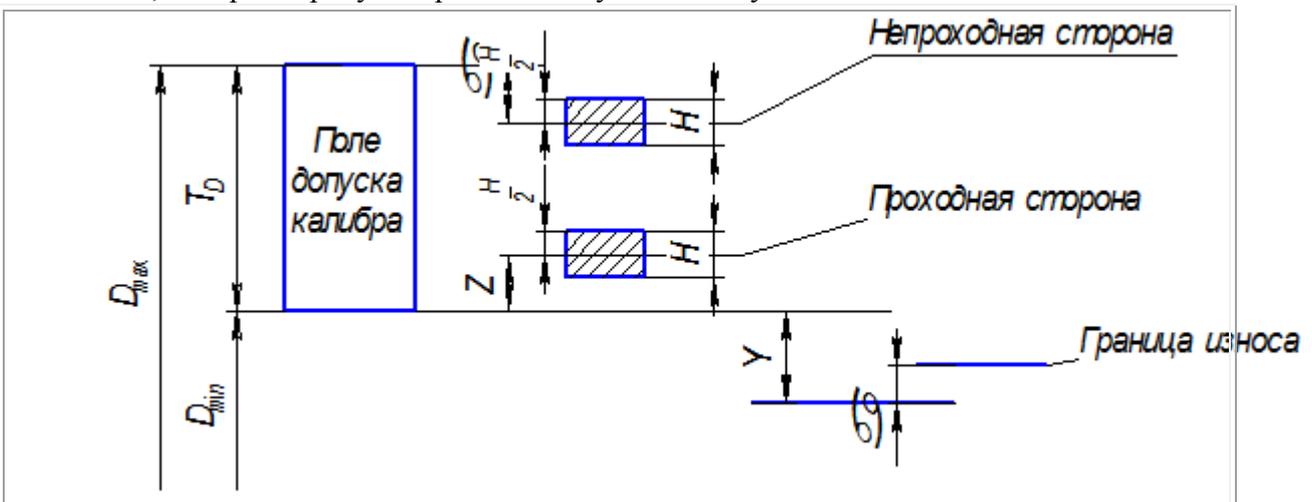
Схема расположения полей допусков калибров для контроля отверстий
